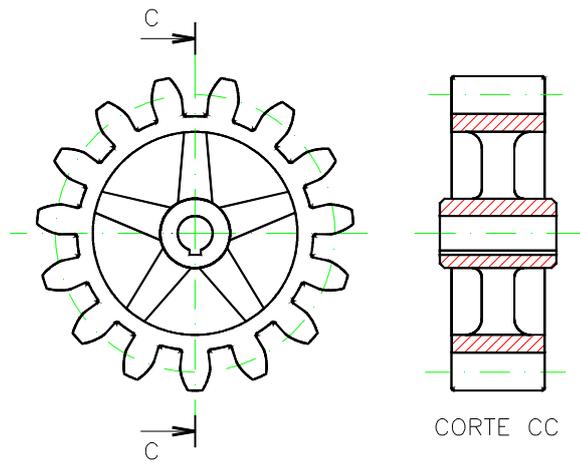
engrenagem com 5 (cinco) braços e 15 (quinze) dentes representada em corte com rotação; o corte mostra os braços e os dentes em verdadeira grandeza.
